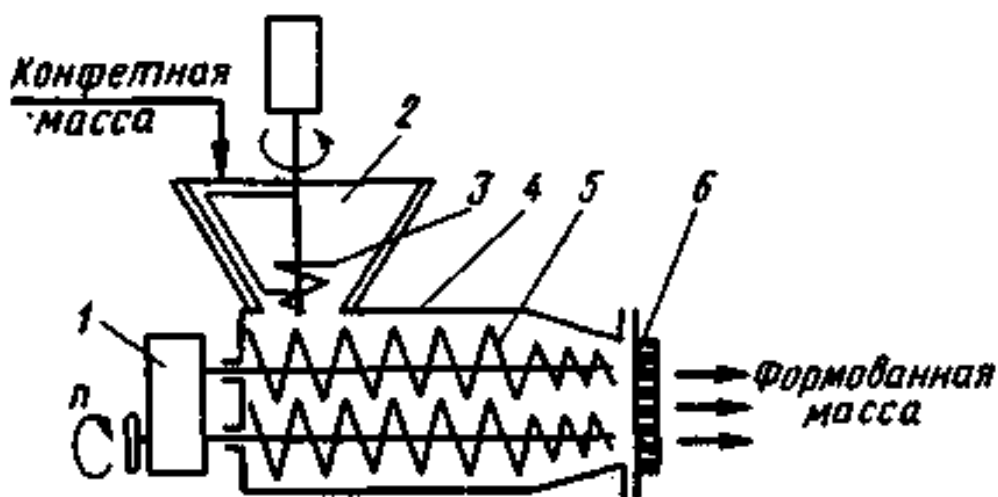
Схема двухшнекового формовочного прессы:
